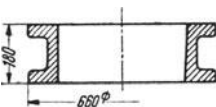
Zwischenstück (Werkzeichnung und Verkaufriß; innen Formschräge = Kegel).
